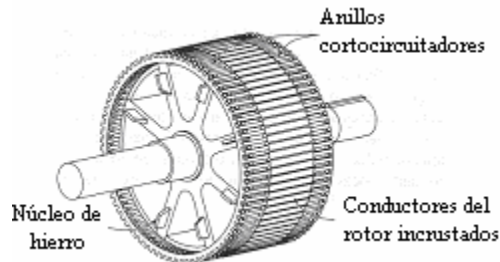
Rotor Jaula de Ardilla. Fuente: (Ebel, Idler, Prede, & Scholz, 2008)
